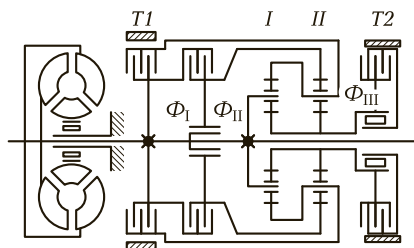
Схема гидромеханической передачи с планетарной коробкой передач:
